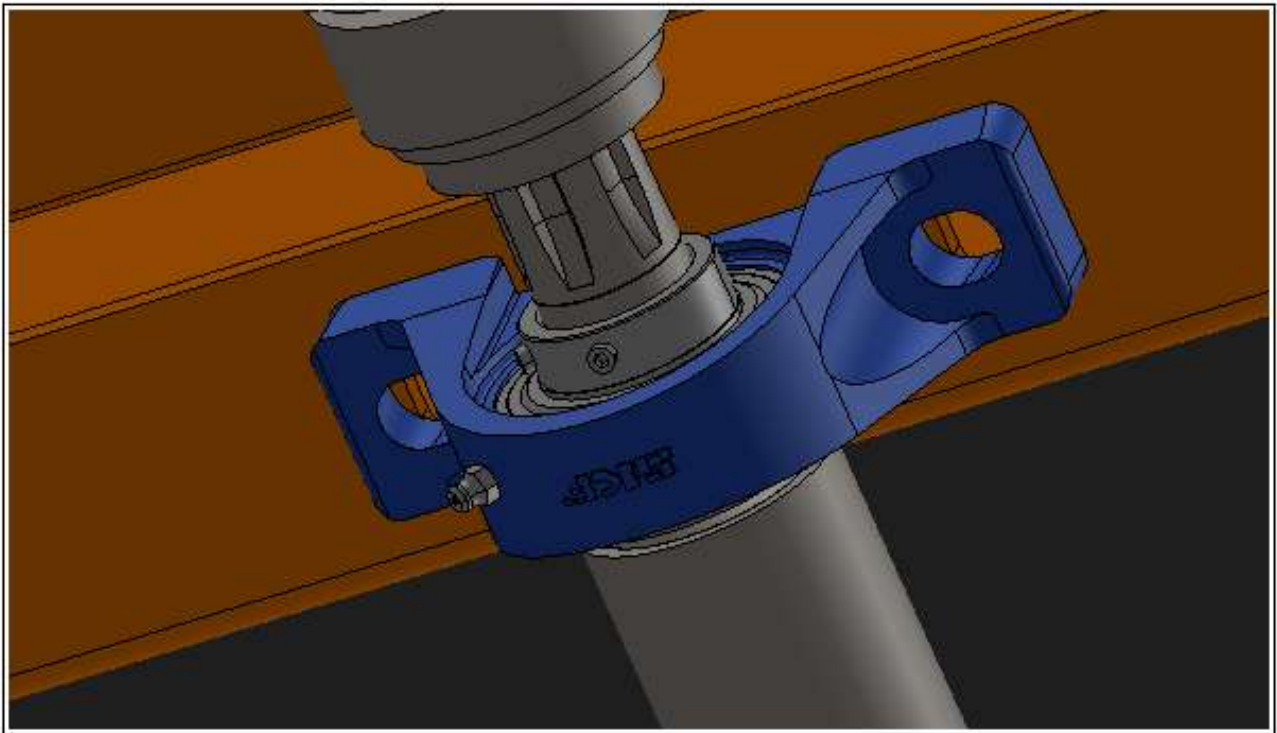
Bancadas sobre las que se halla montado el eje fijo.
